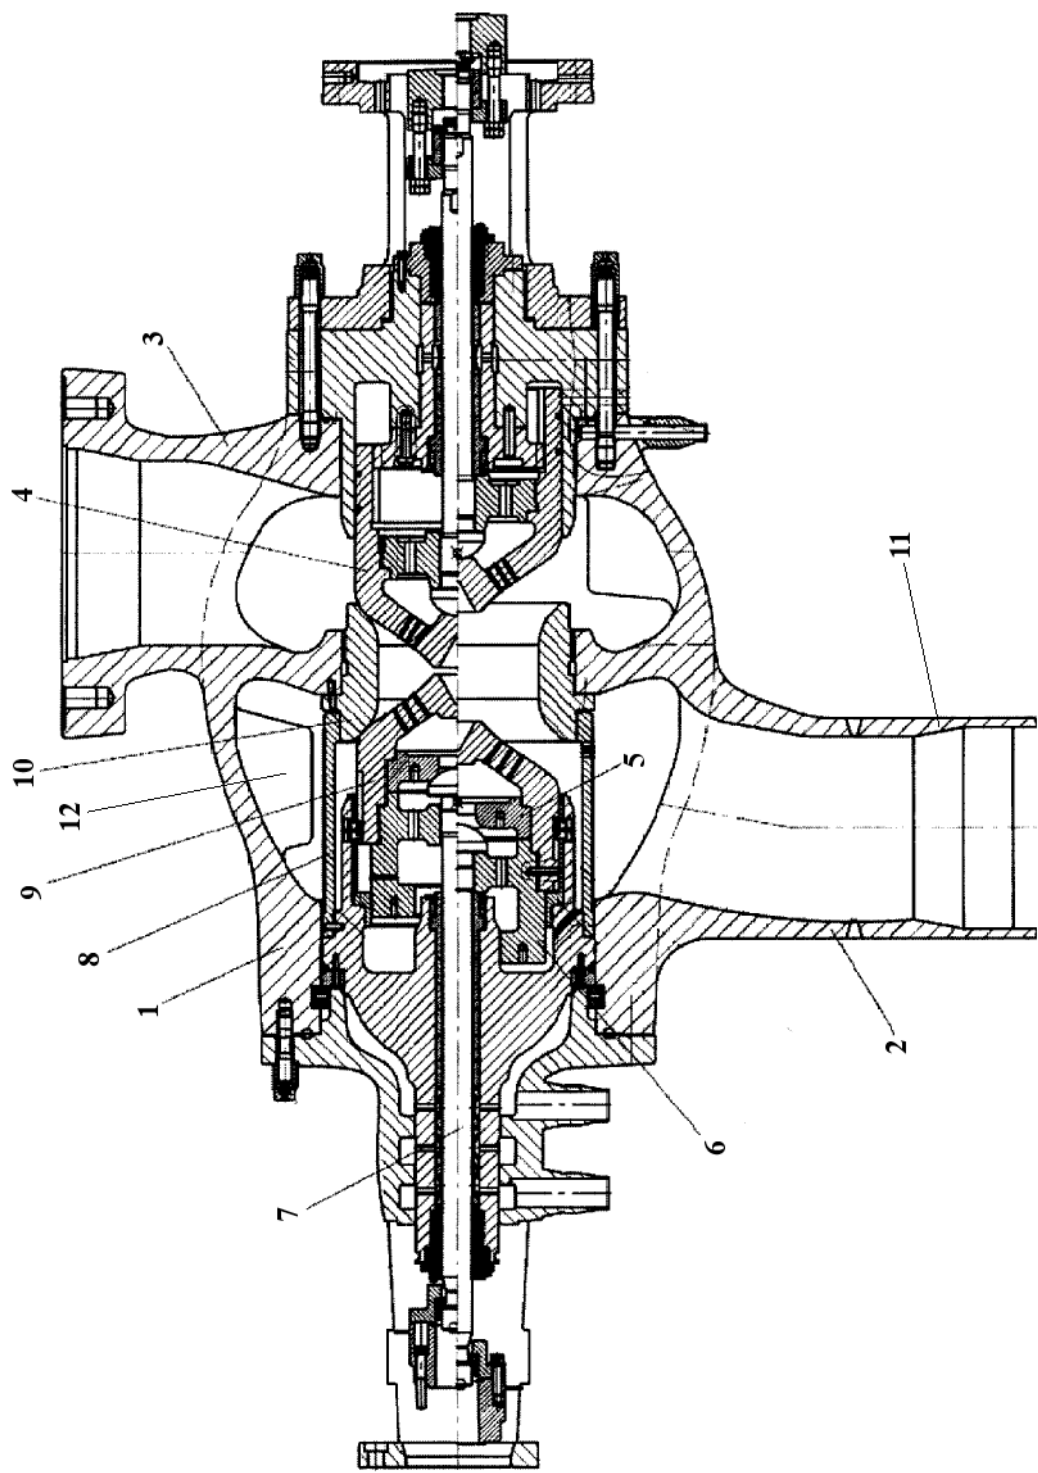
Стопорно-регулирующий клапан: 1 – корпус, 2 – входной патрубок, 3 – выходной патрубок, 4 – стопорный клапан, 5 – седло разгрузочного клапана, 6 – гайка, 7 – шток разгрузочного клапана, 8 – защитная сетка, 9 – регулирующий клапан, 10 – седло, 11 – опорная втулка, 12 – противовихревое ребро
